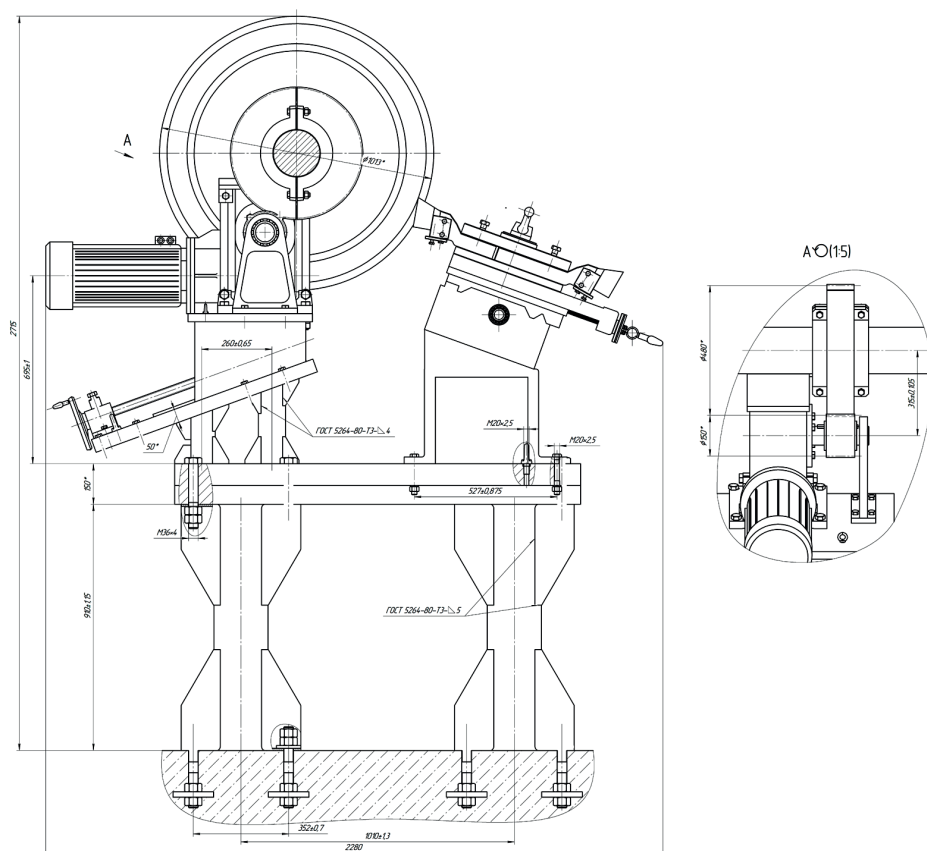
Устройство для обработки колесных пар в сборе [2]
